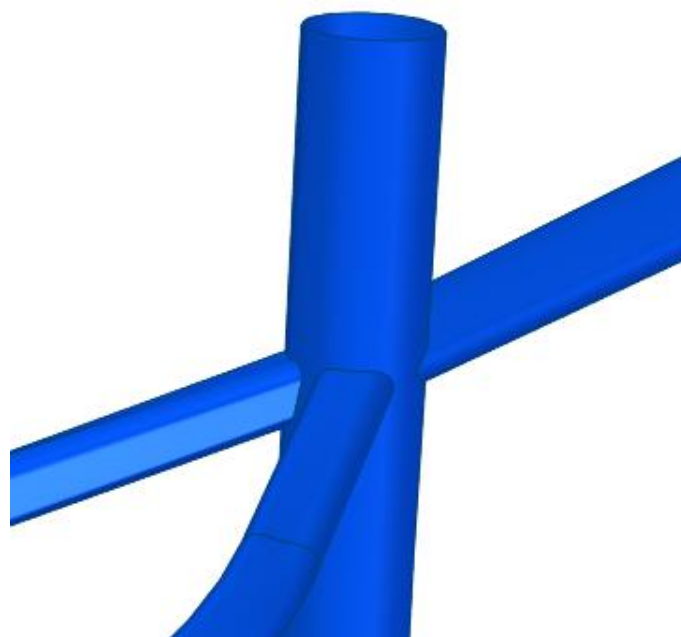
Modelo con tubos de aluminio soldado. Vista isométrica.
